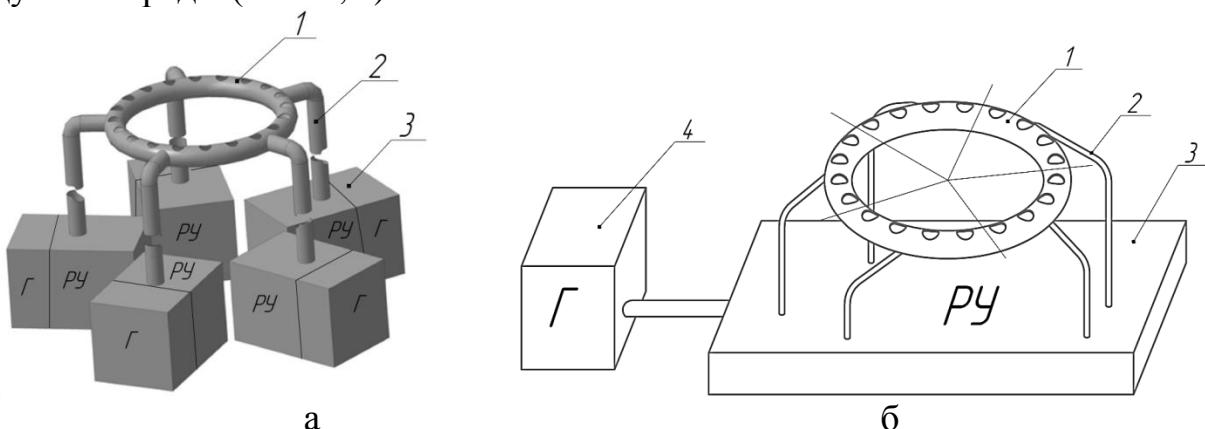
Конструкция секционной насадки: а – с индивидуальными источниками подачи воздушной среды, б – с регулирующим устройством, 1 - насадка, 2 – трубопровод, 3 - регулирующее устройство, 4 - генератор подачи воздушной среды
